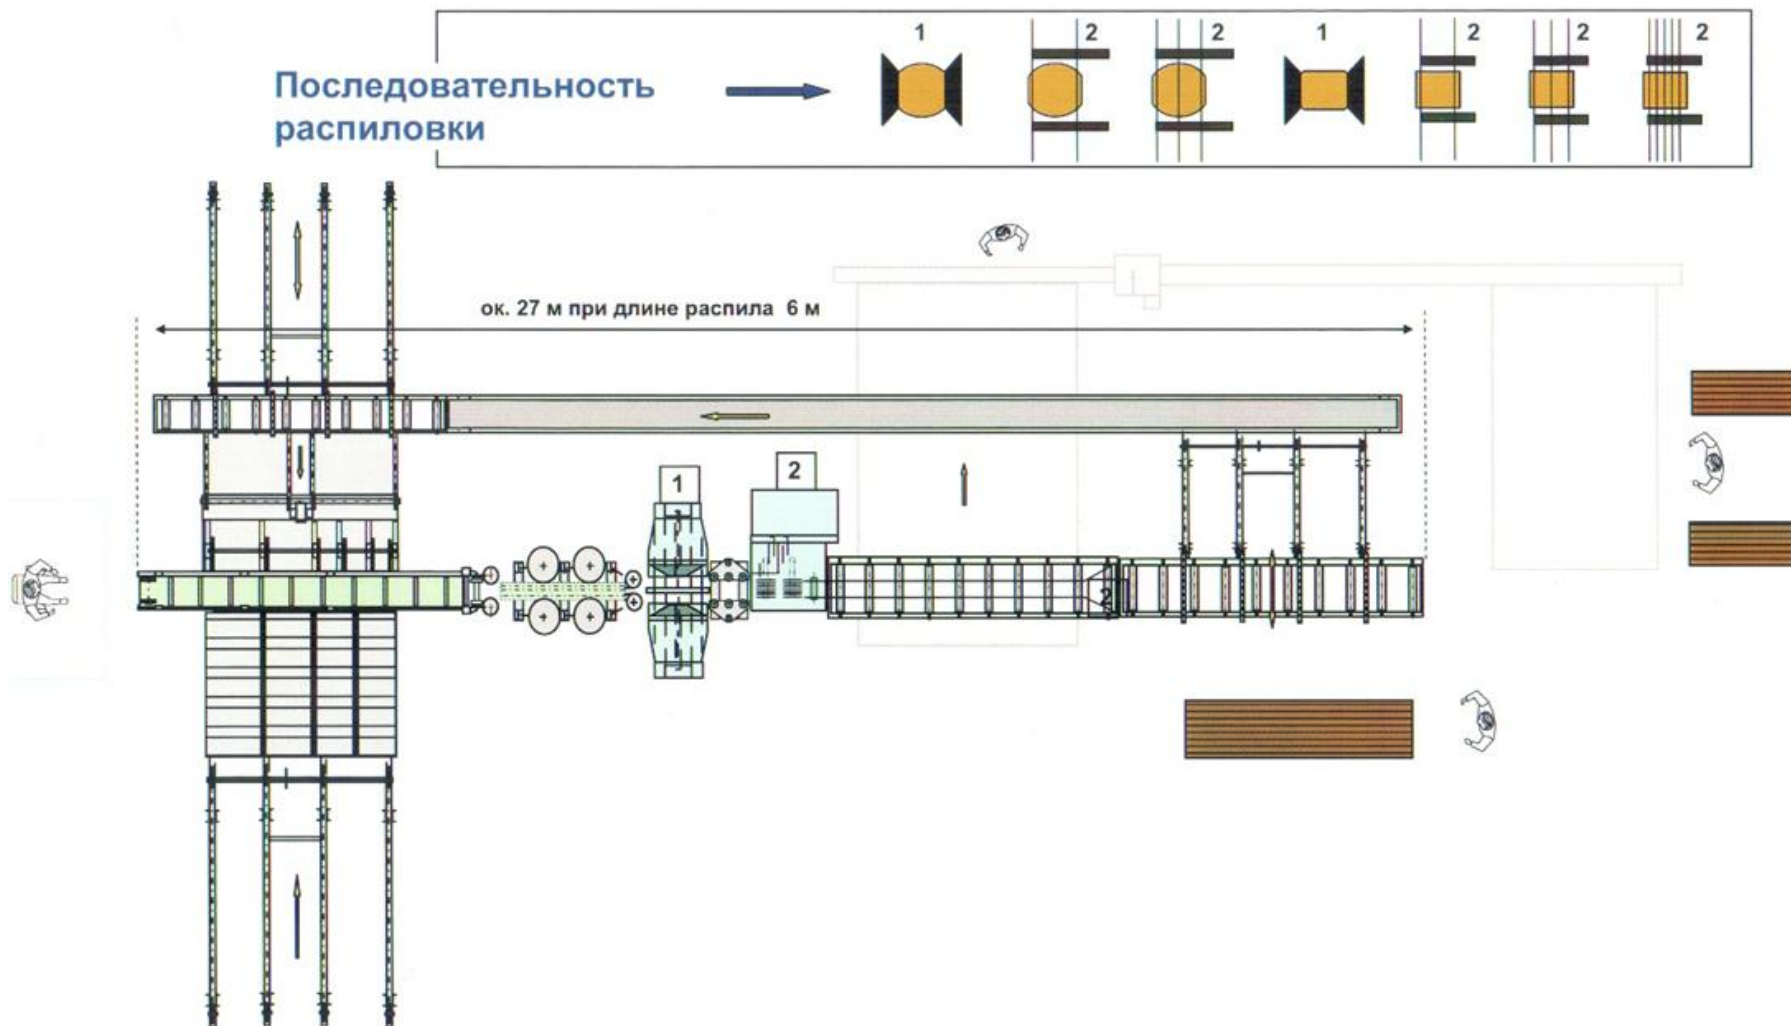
Фрезерно-брусующая установка с круговой подачей сортиментов с двухшпindelным круглопильным станком, производительностью 30-80 тыс. м³ бревен в год /9/
